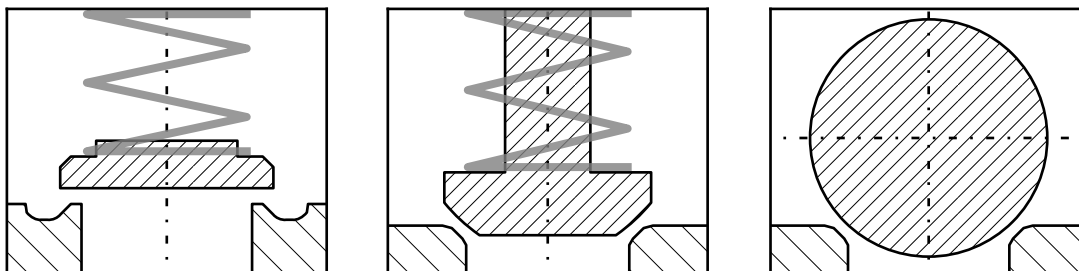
Druckgesteuerte Ventile: Platten- und Kegelventil (befedert) sowie ein Kugelventil (unbefedert)
